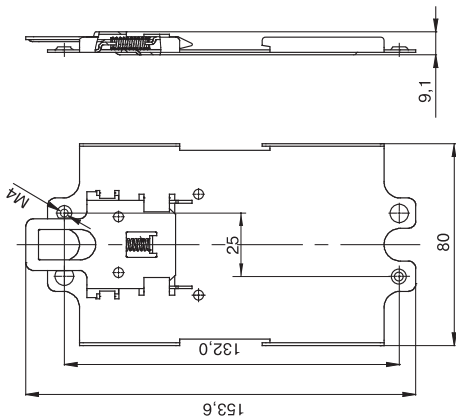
Адаптер для крепления выключателя AE2040M на стандартную 35 мм рейку
